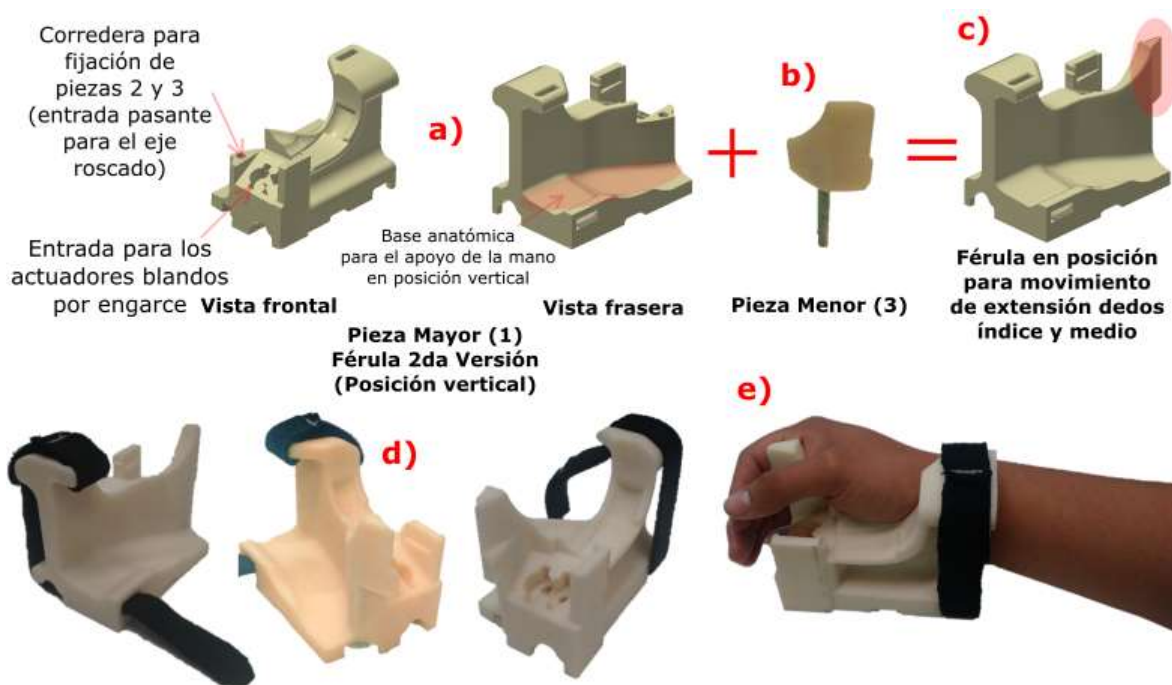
Configuración de la segunda versión de la férula para el movimiento de oposición del pulgar. a) Pieza mayor de la férula, b) Pieza menor desmontable de la férula, c) Ensamble final visto desde atrás del ensamble con la pieza menor resaltada en rojo, d) Férula ensamblada, y e) Mano posicionada y sujeta en la férula mediante neopreno
